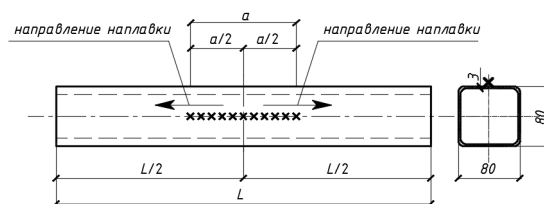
Схема расположения и направления наплавки холостых валиков
